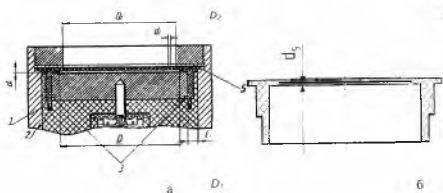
Схема конструкции изоляции катода (а) и фторопластовой прокладки (б)
